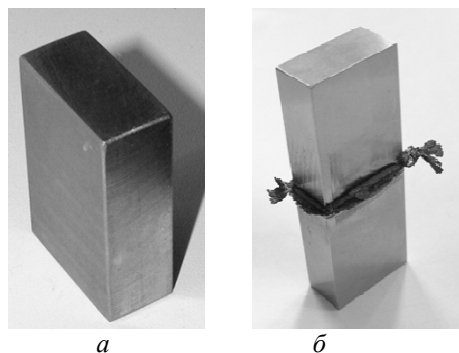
Образцы сплава ЭП742: а – до сварки; б – после ЛСТ
